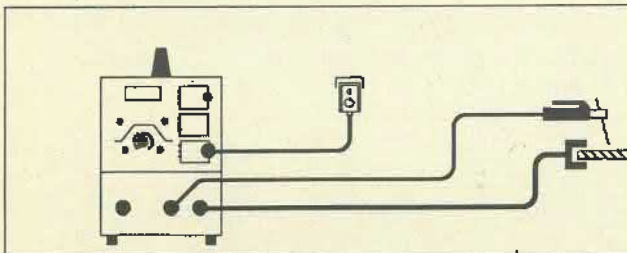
TRANSTIG 200 als ELEKTRODEN-Handschweißgerät bestehend aus: Stromquelle, Elektroden-Handkabel, Massekabel (Fernregler TP2 wahlweise).
